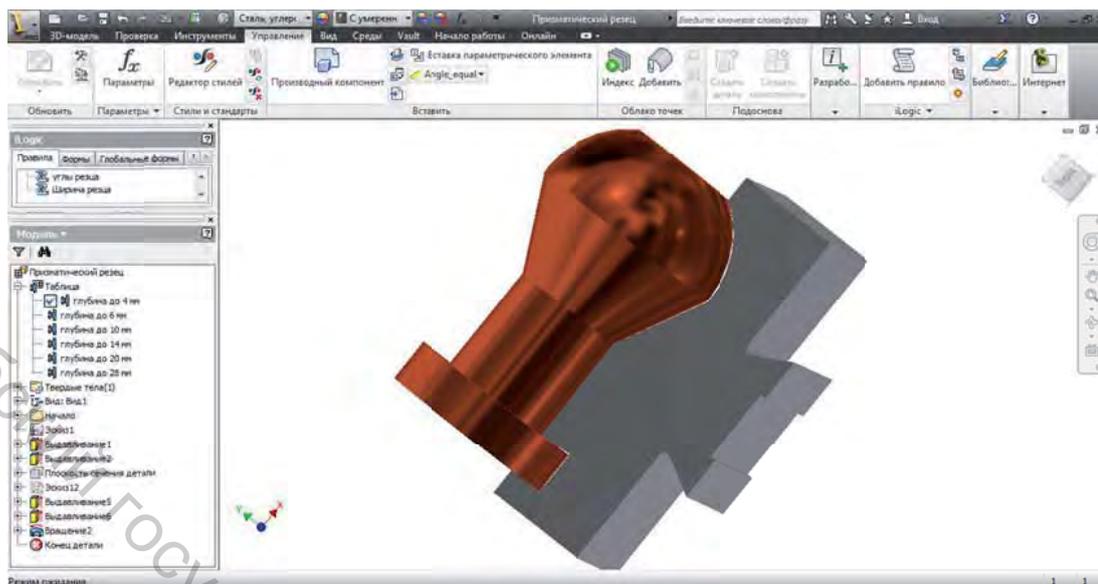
Трёхмерные модели призматического фасонного резца и детали заданного профиля
